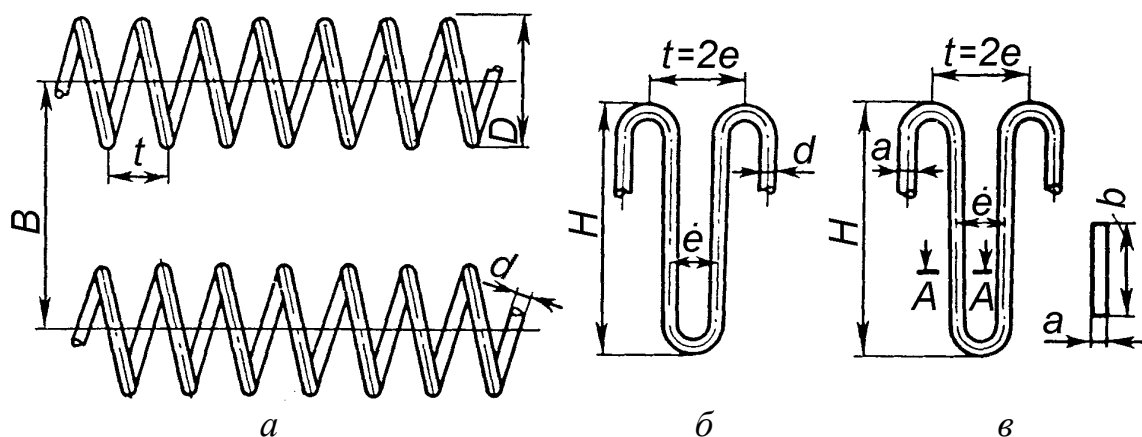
Типы конструкций металлических нагревателей: *a* — проволочная спираль (п.с.); *б* — проволочный зигзаг (п.з.); *в* — ленточный зигзаг (л.з.)
